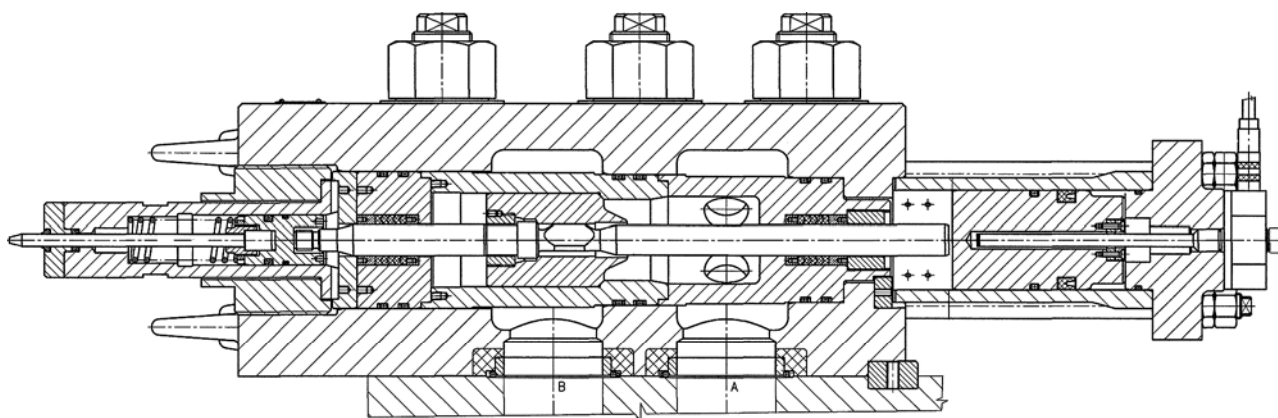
Конструкция запорно-регулирующего клапана стыкового исполнения с декомпрессором
